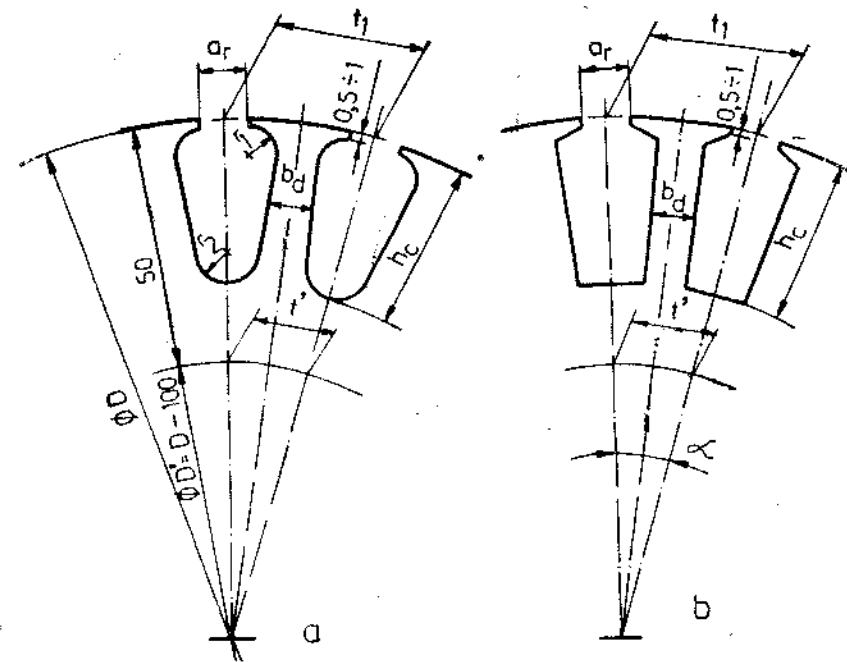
Forme constructive ale creștăturilor ovale (a) și trapezoidale (b) pentru indus, dinți avînd pereții paraleli (lățimea constantă).
